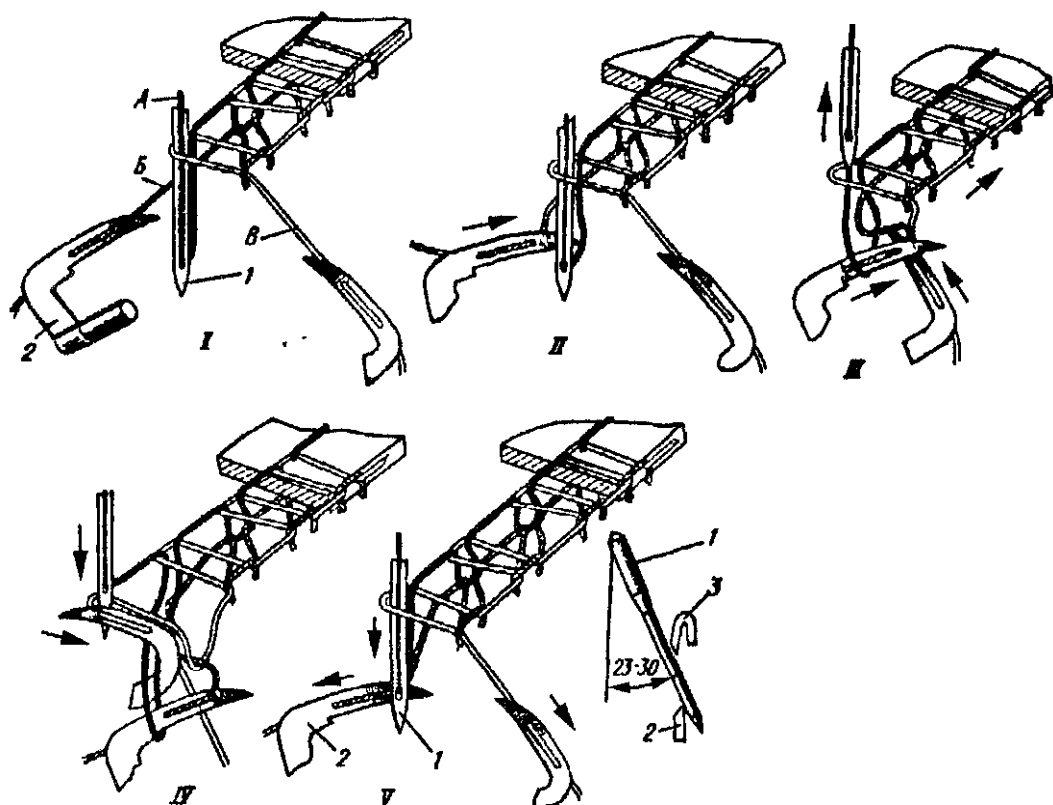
Схема образования трехниточного краеобметочного стежка
